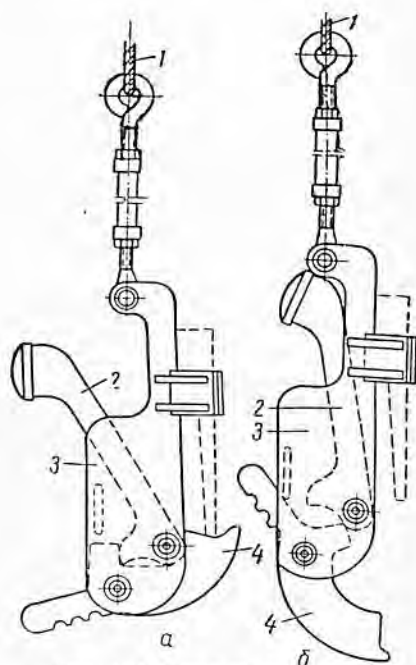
Крюк-сбрасыватель. а — крюк-сбрасыватель в варяженном виде; б — крюк-сбрасыватель в рабочем виде; 1 — стальной трос; 2 — курок; 3 — корпус; 4 — опора.
